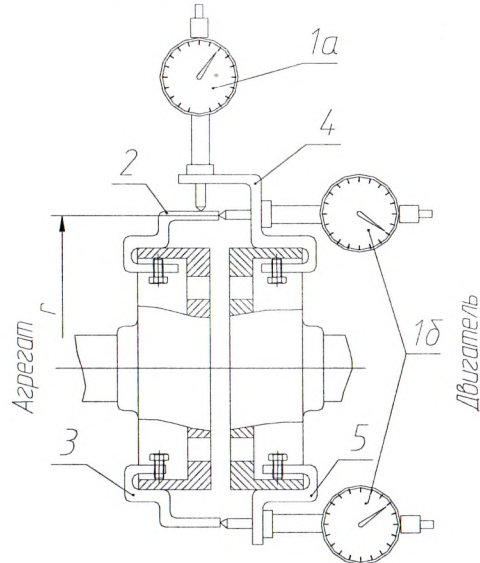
Приспособление для центровки, укрепленное на ободах полумуфт.
